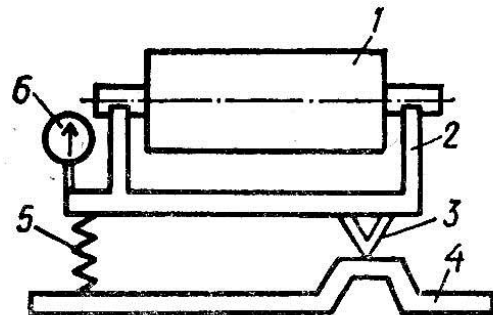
Пристрій (стенд) для динамічного балансування деталей (вузлів)
